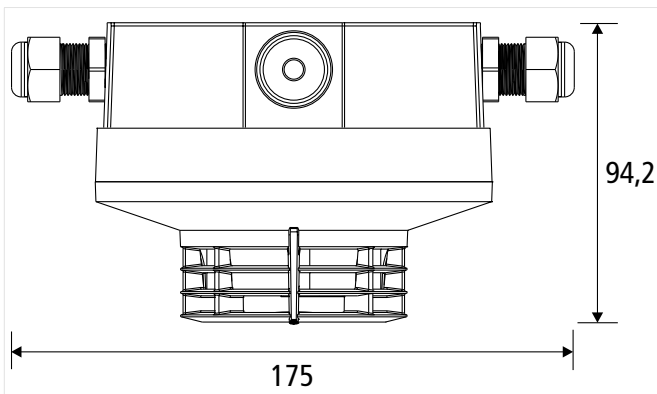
Seitenansicht mit Sockel USB 502-7 Ex-i
